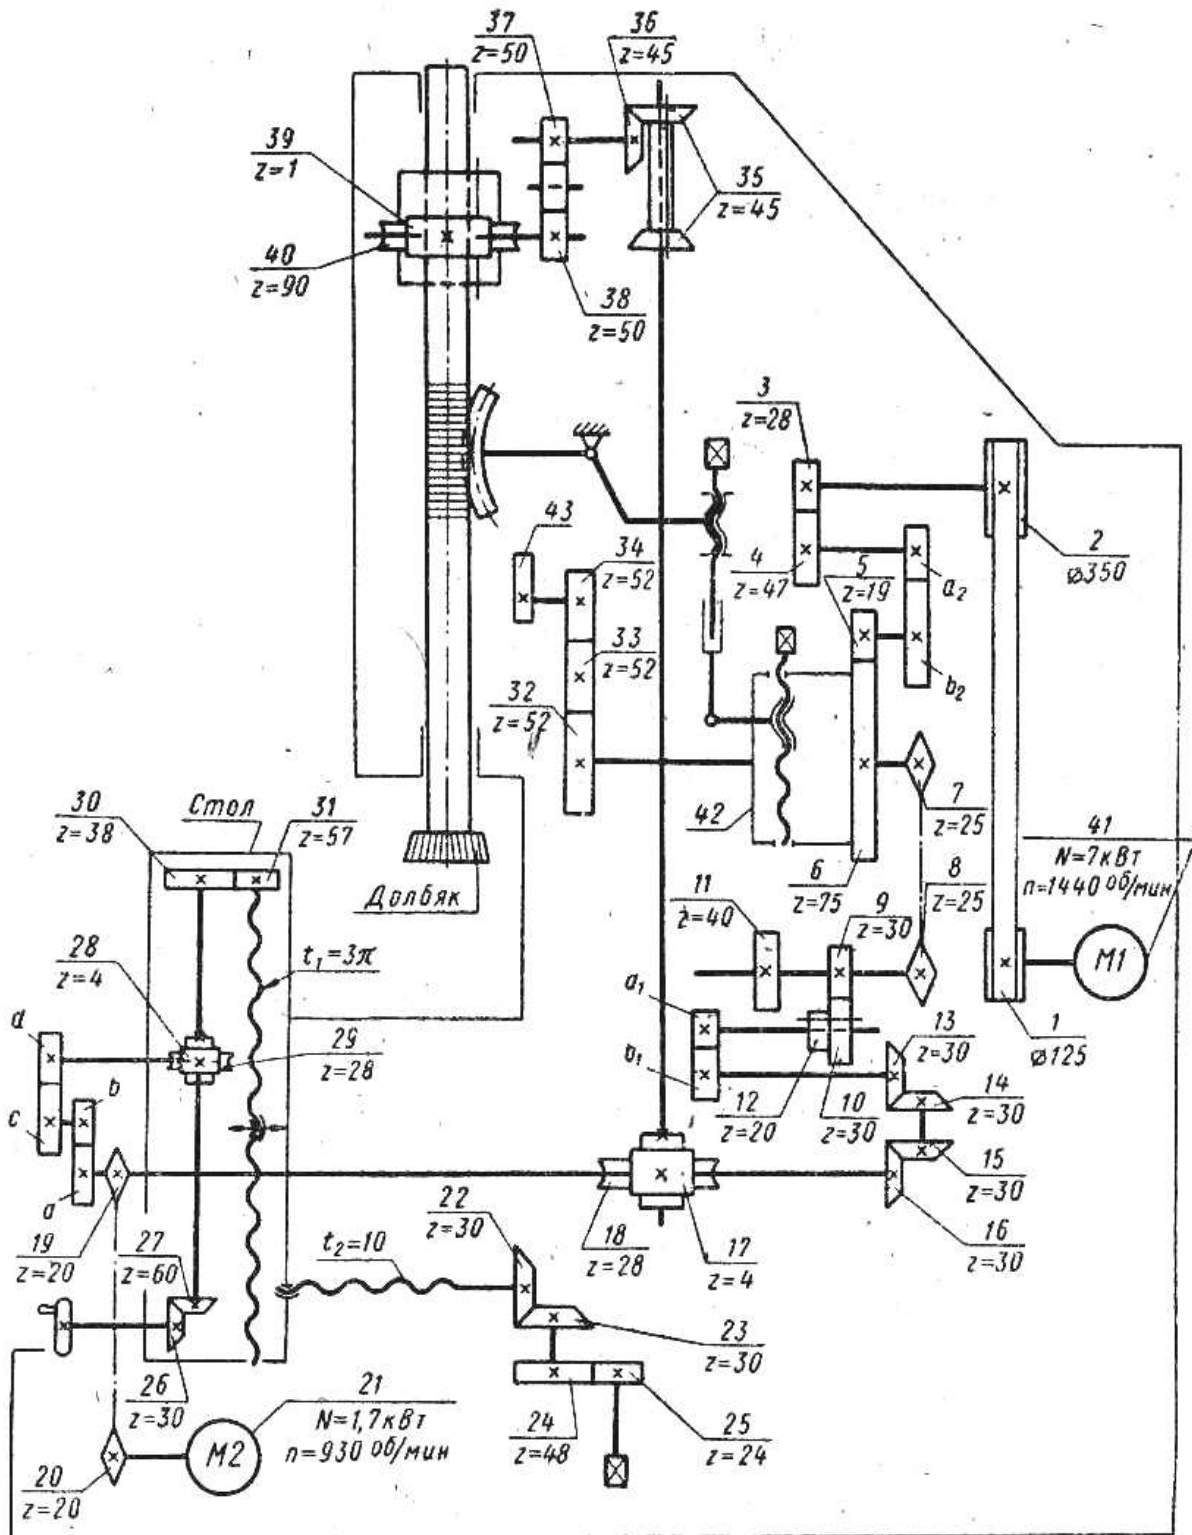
Кинематическая схема долбежно-реечного станка
